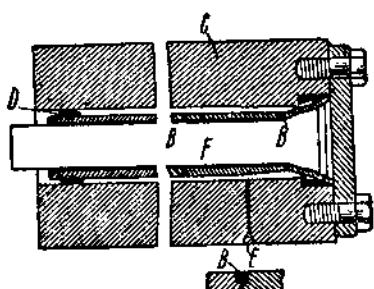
Сварной кокиль, установленный для исправления.
